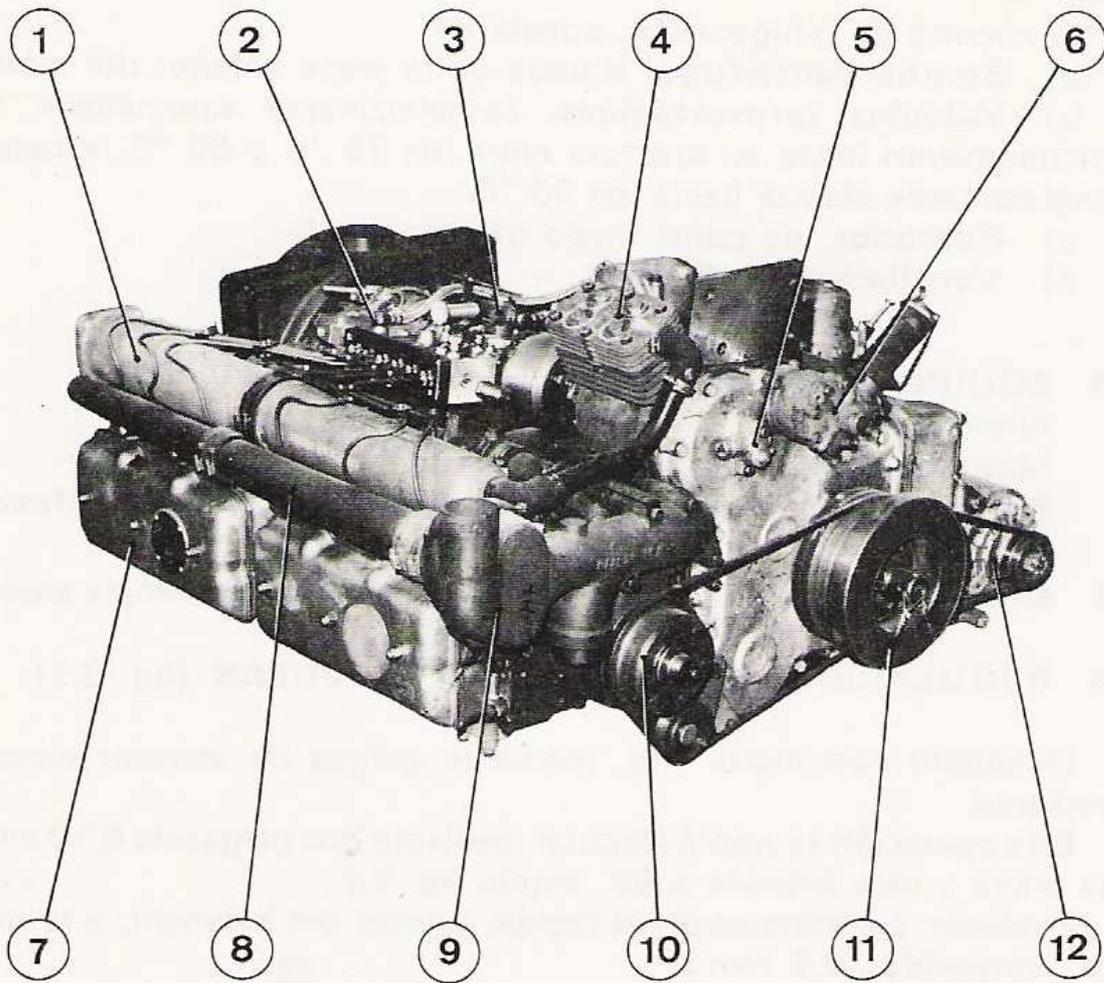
Motor 9152/2 (lado izquierdo)
